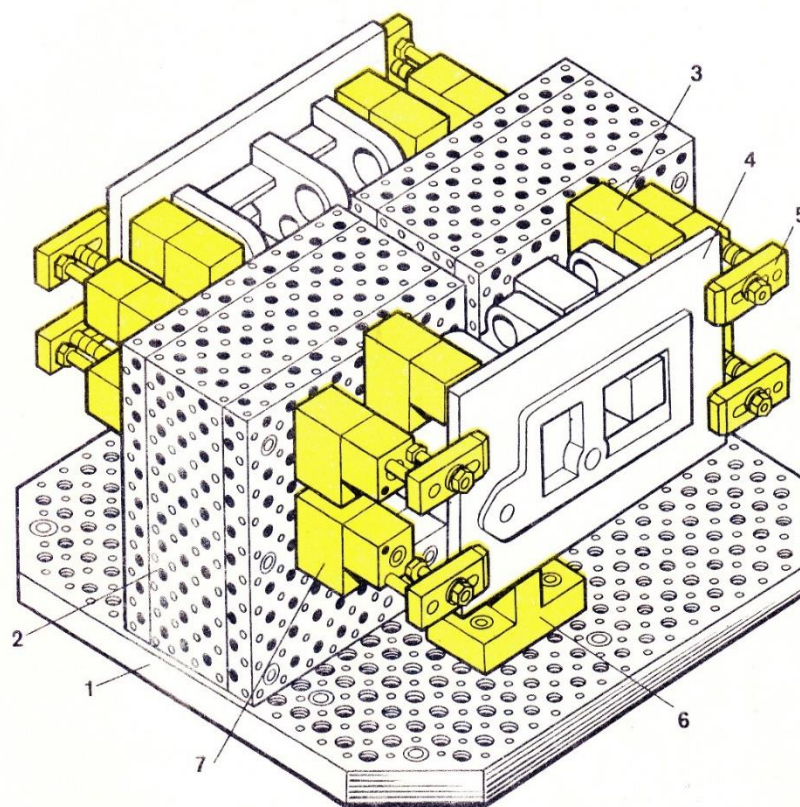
Двухместное АСП с горизонтальными гидроцилиндрами
